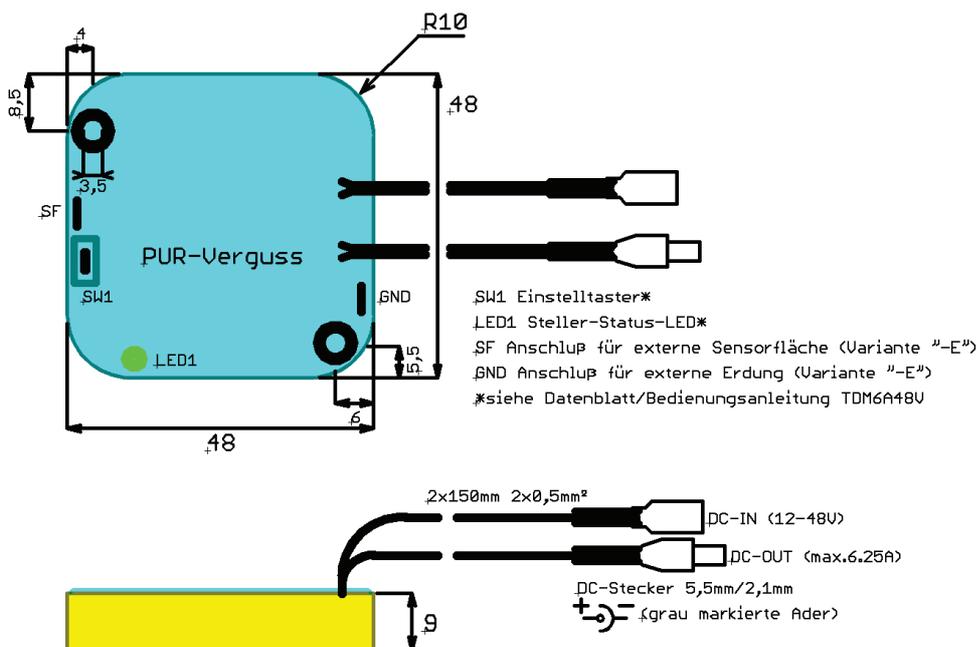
Abmessungen (Angaben in mm) TDM6A48V mit DC-Anschlußleitung
